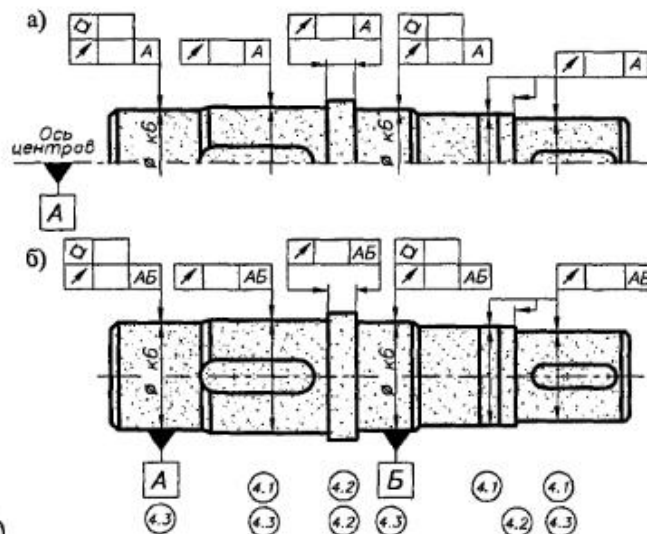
Обозначение допусков формы и расположения поверхностей вала, когда:
